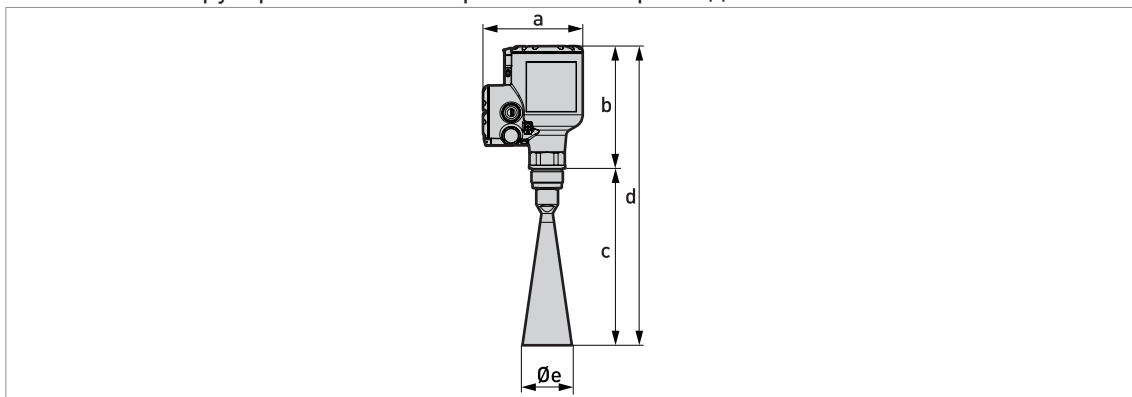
Металлические рупорные антенны с резьбовыми присоединениями G или NPT
